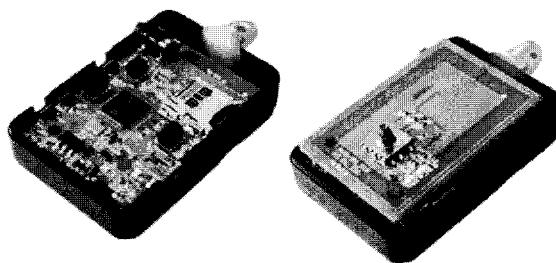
케이스와 PCB 조립 모습 (좌) 메인회로부 PCB 장착모습 (우) RFID 회로부까지 장착한 모습
